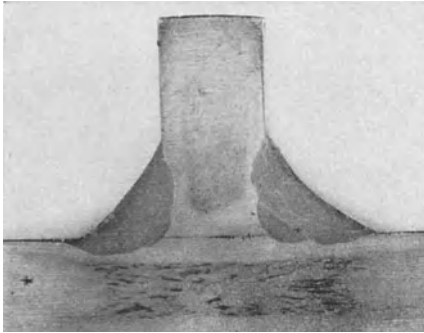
Gute elektrische Kehlnaht-Schweißungen.
